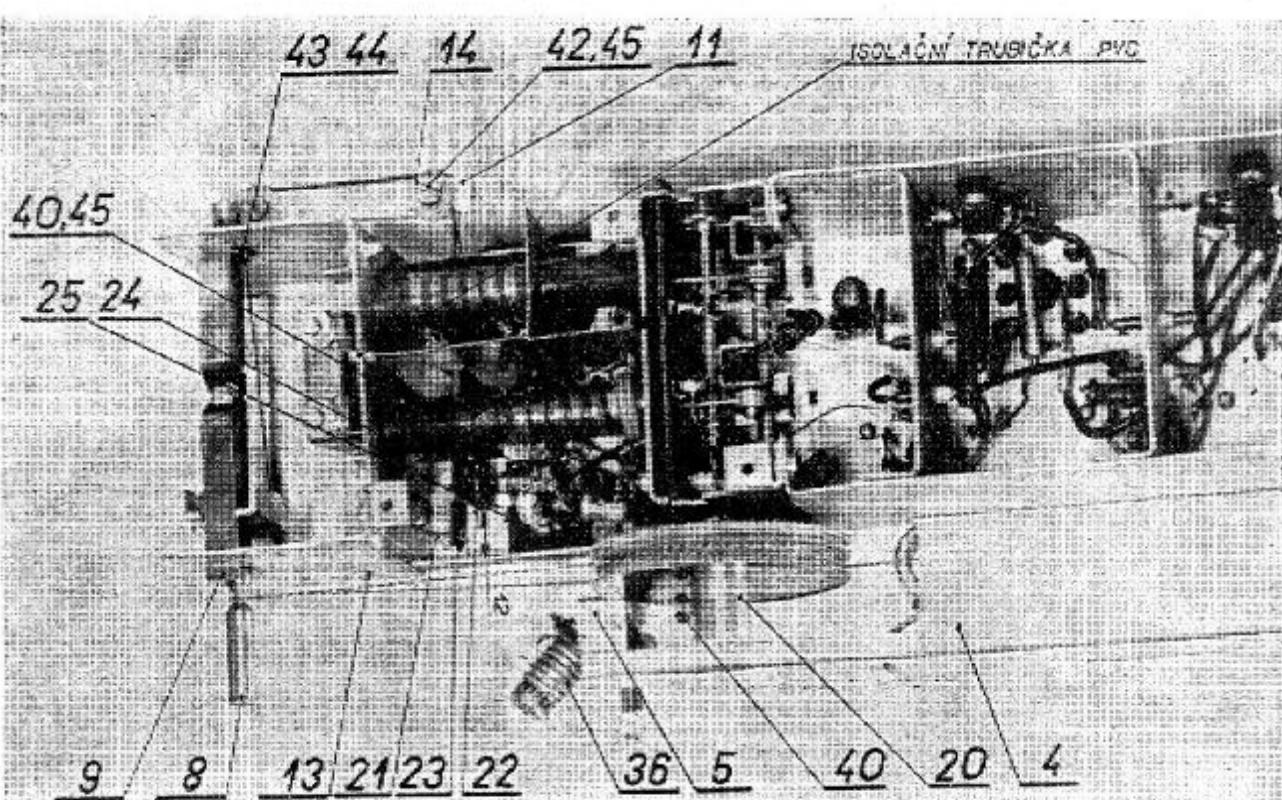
Kótovaná sestava označení elektroniek a filtrov
